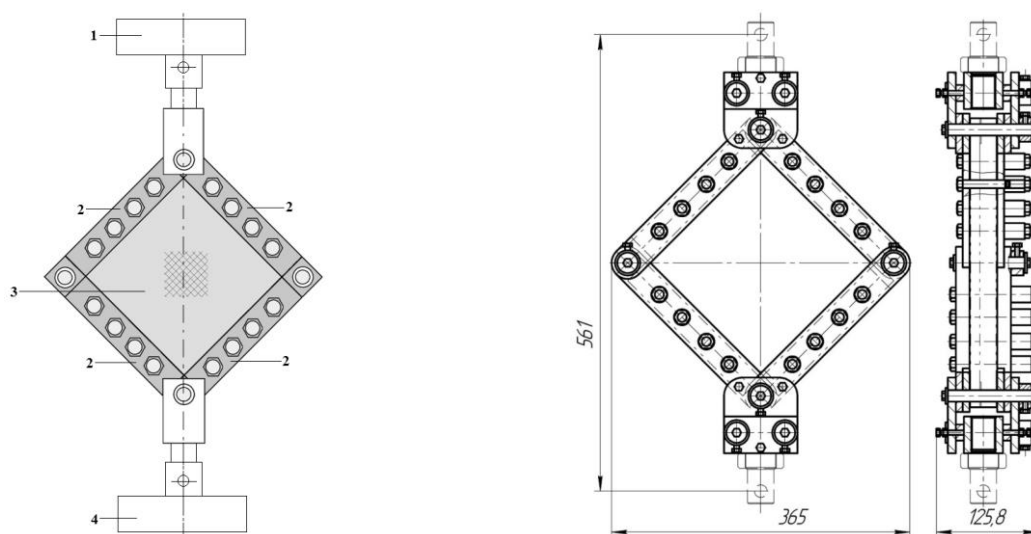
Схема закрепления и эскиз оснастки для проведения испытаний образцов-панелей на сдвиг (1 – подвижная траверса; 2 – захваты (шарнирная рама); 3 – образец; 4 – неподвижная траверса)
